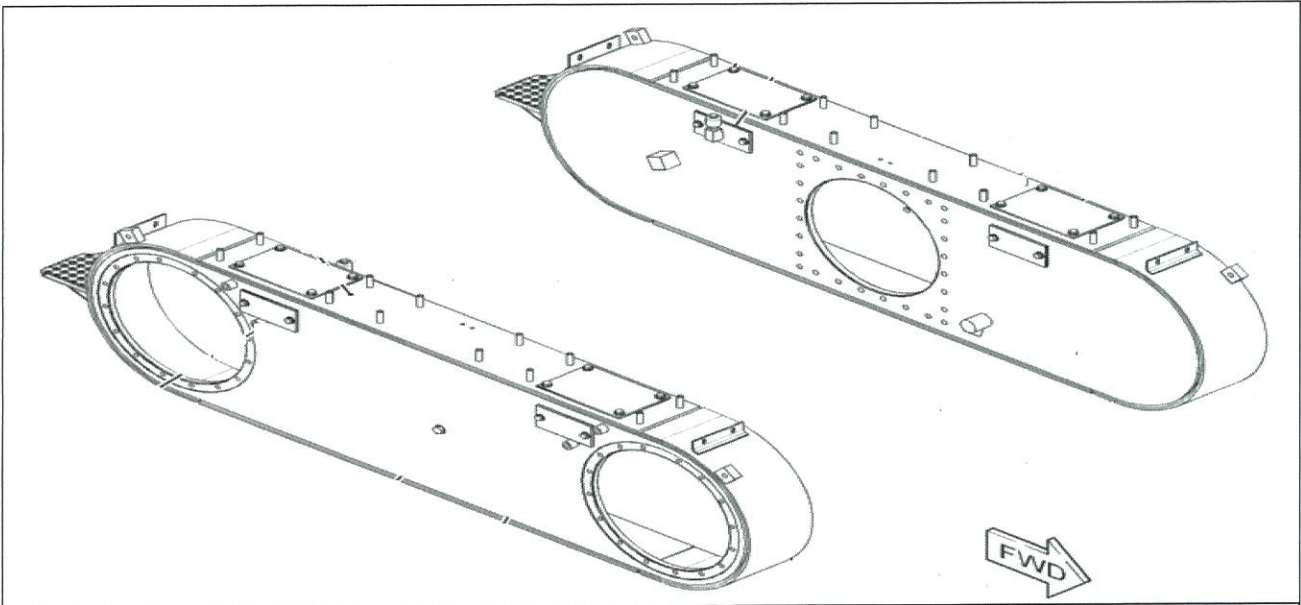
Revisar fisuras, fugas de aceite y daños en la estructura.
